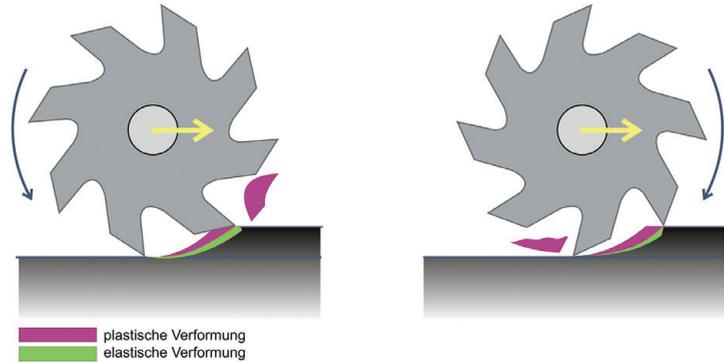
Laufrichtungen beim Fräsen: links: Gegenlaufräsen, rechts: Gleichlaufräsen
